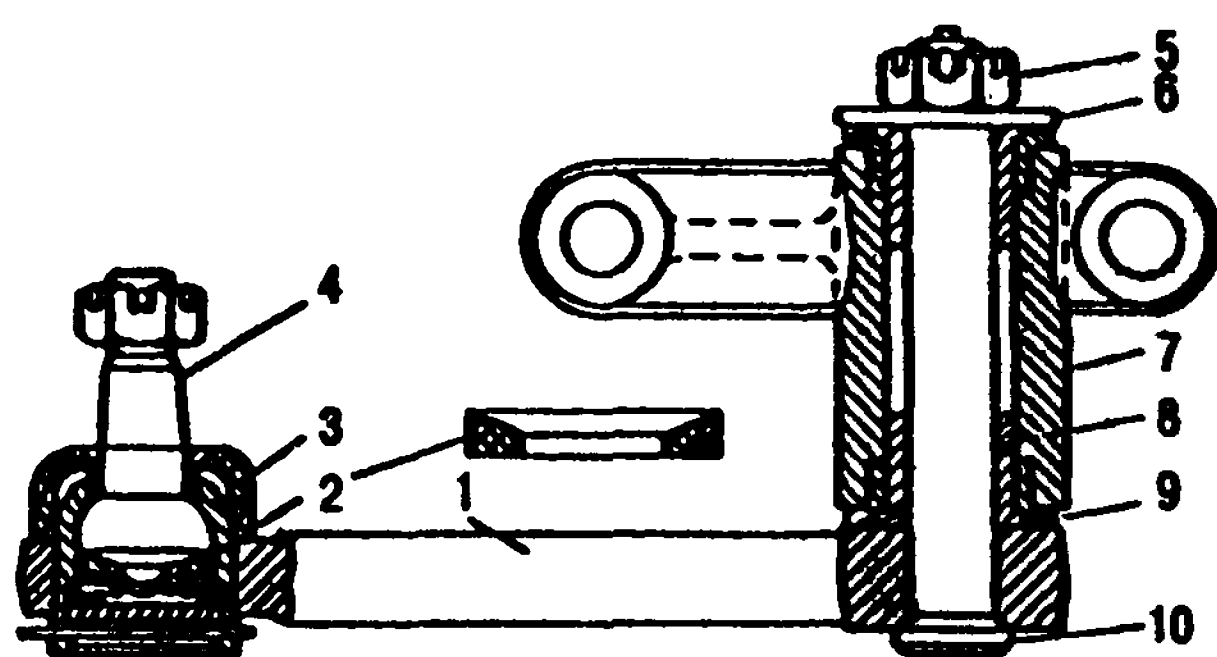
Маятниковый рычаг: 1 - рычаг; 2 - сухарь; 3 - корпус шарнира; 4 - шаровой палец; 5 - гайка; 6 - шайба; 7 - кронштейн; 8 - втулка; 9 - резиновая защитная втулка; 10 - палец
